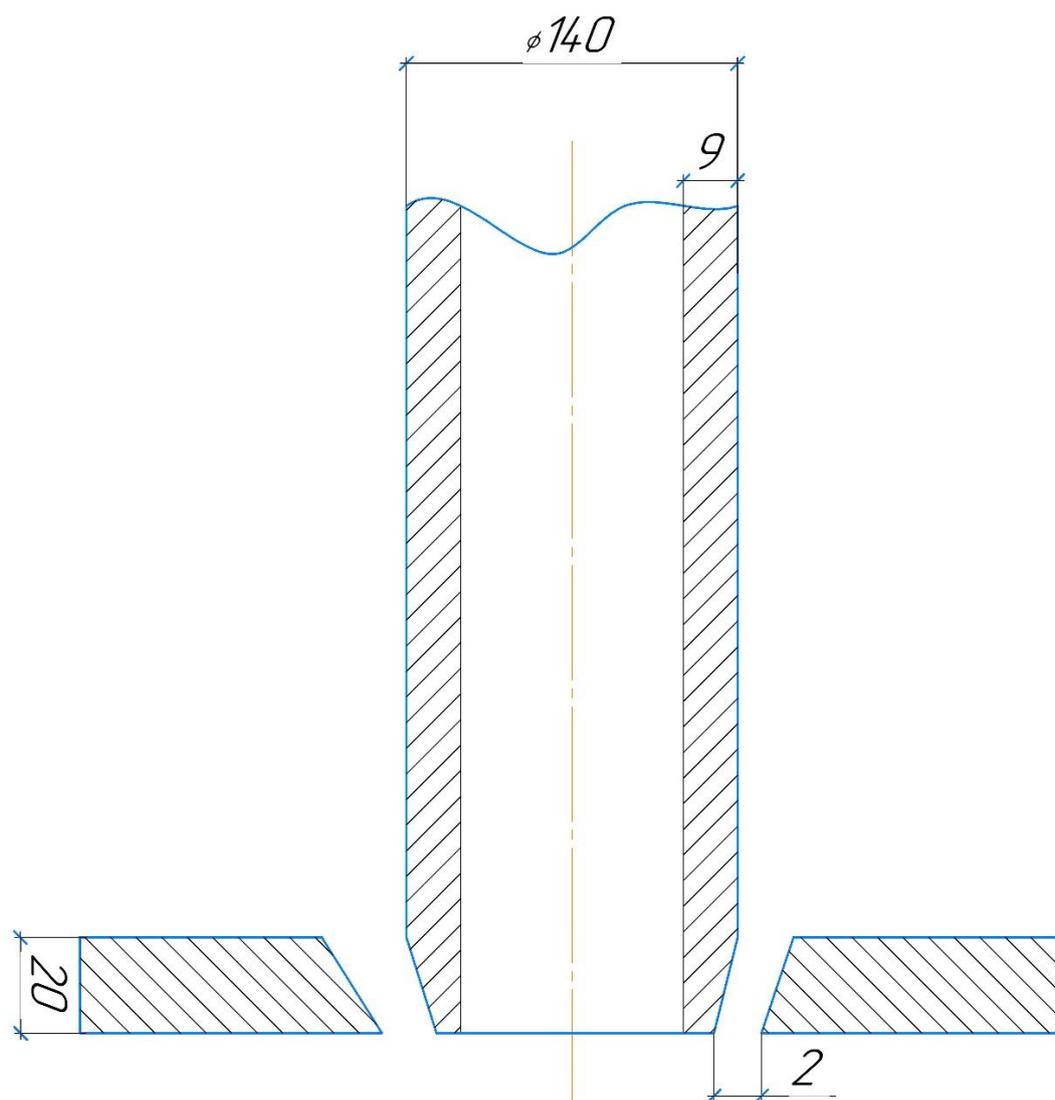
Стойка с плитой перед сваркой
